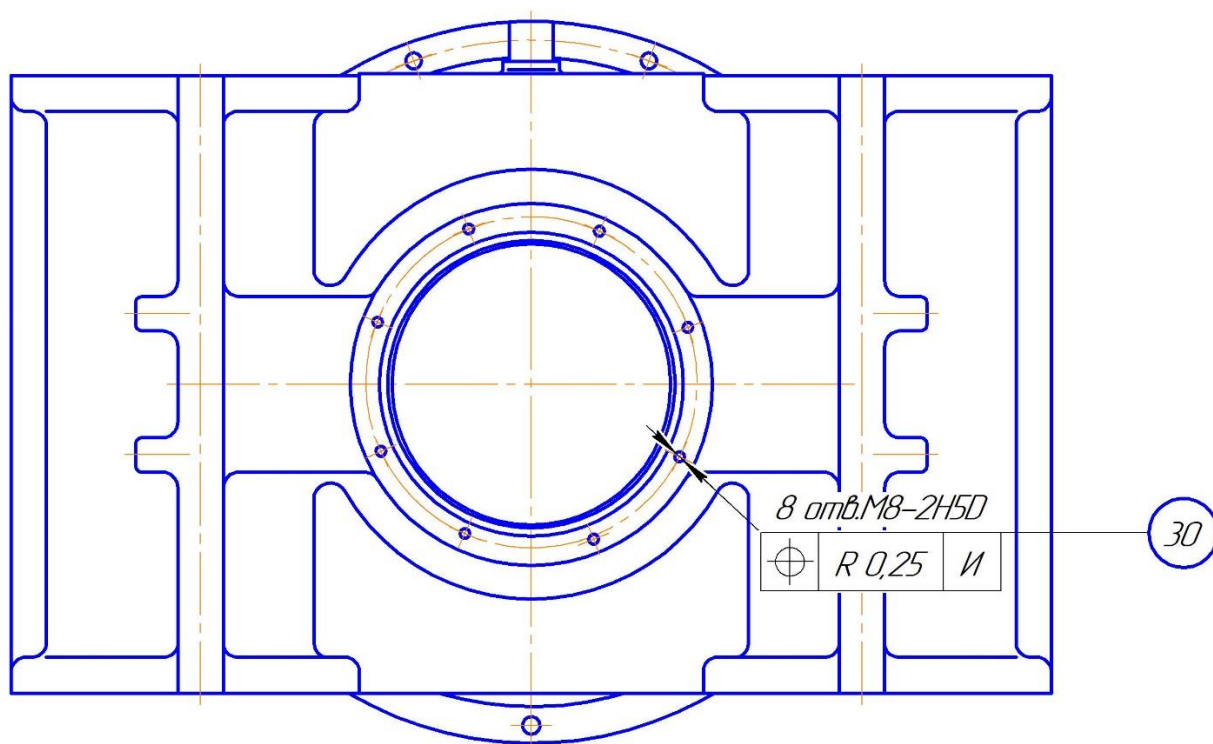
Главный вид. Нумерация поверхностей детали «Корпус охладителя»
